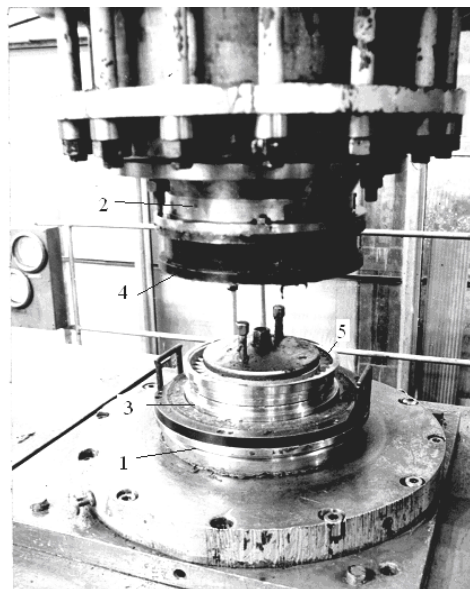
Вид рабочей зоны с установленной заготовкой в приспособлении
